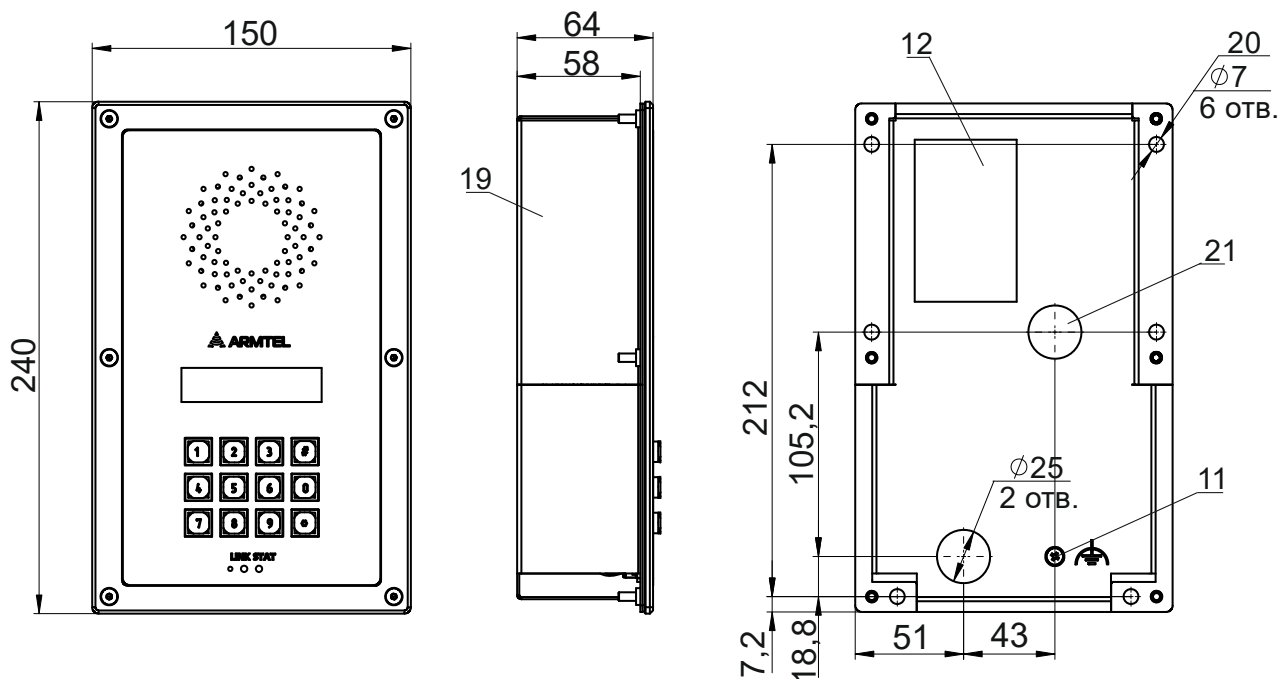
Внешний вид и габаритные размеры CCS-IP3 (начало)
